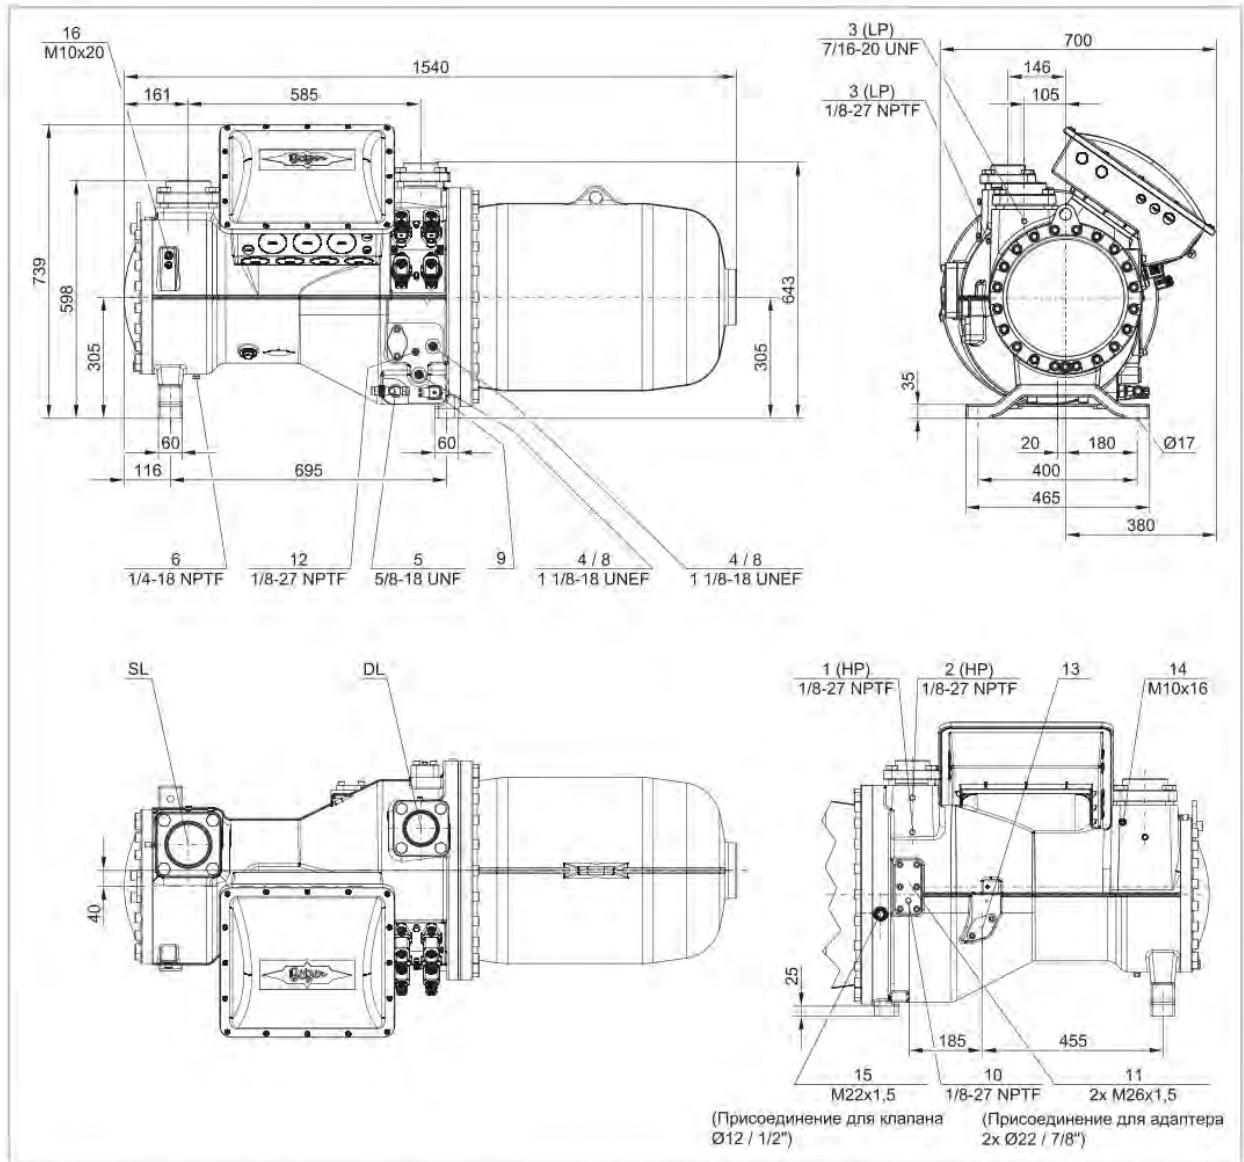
Чертежи с указанием размеров для компрессоров CSH8553-80Y .. CSH8593-180(Y)
